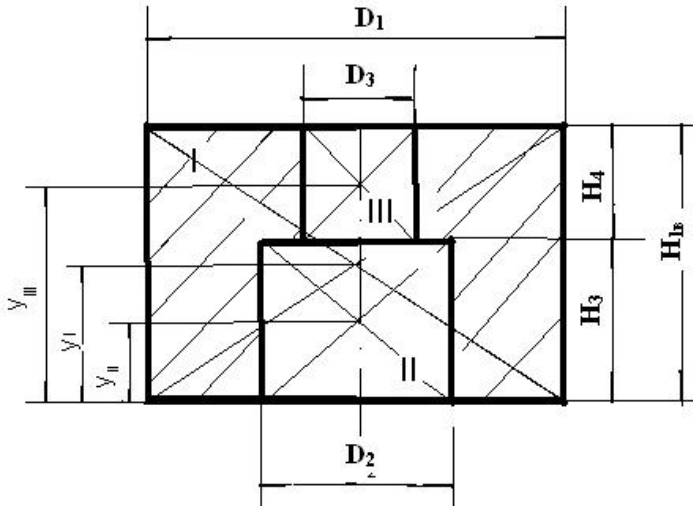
Розбивка перетину верхньої поперечки на окремі фігури
